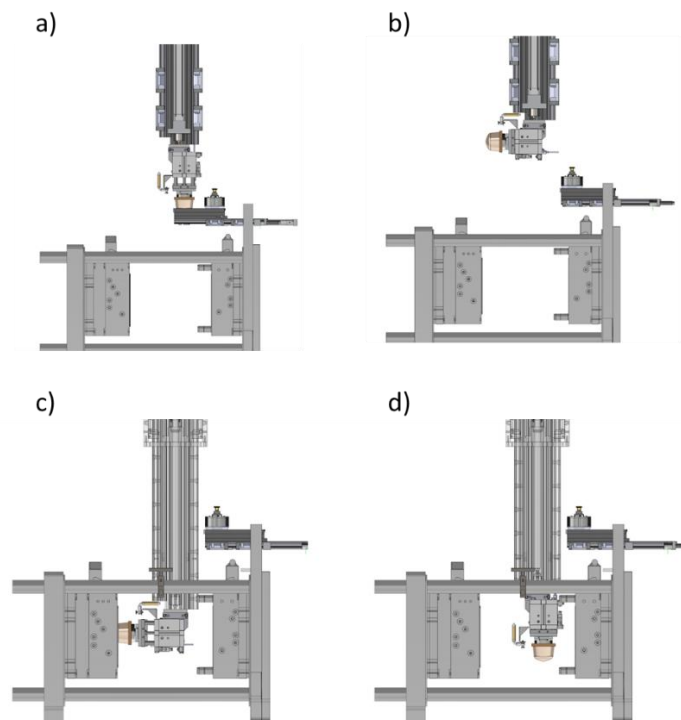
Ausgewählte Maschinenstellungen während des Hybridprozesses: a – Druckstoffaufnahme, b – Vorbereitung zum Einfahren in den Werkzeugraum, c – Druckvorgang auf das Werkzeug, d – IR-Trocknung.
